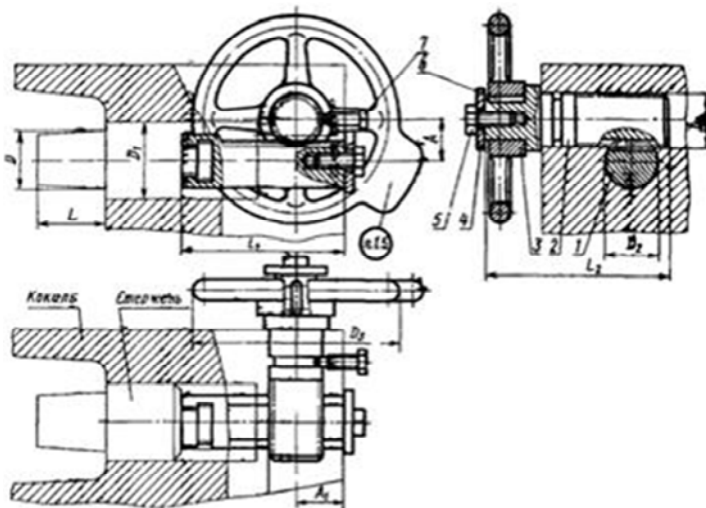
Конструкция реечного приспособления для удаления стержней:
